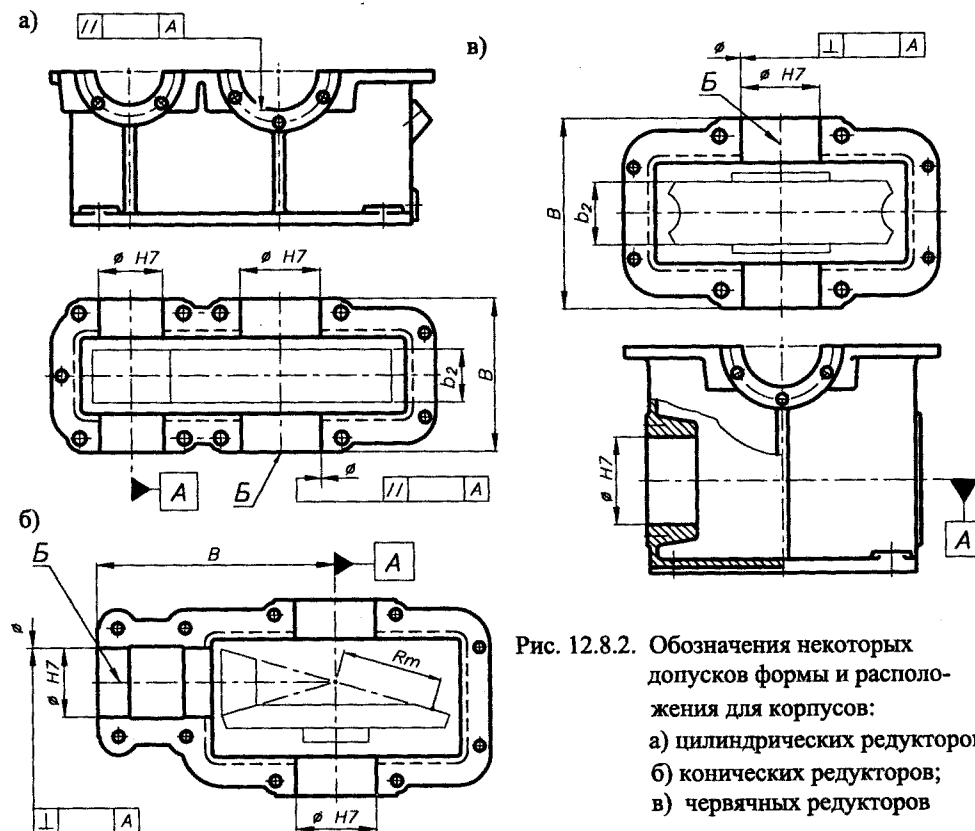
Обозначения некоторых допусков формы и расположения для корпусов: а) цилиндрических редукторов; б) конических редукторов; в) червячных редукторов
